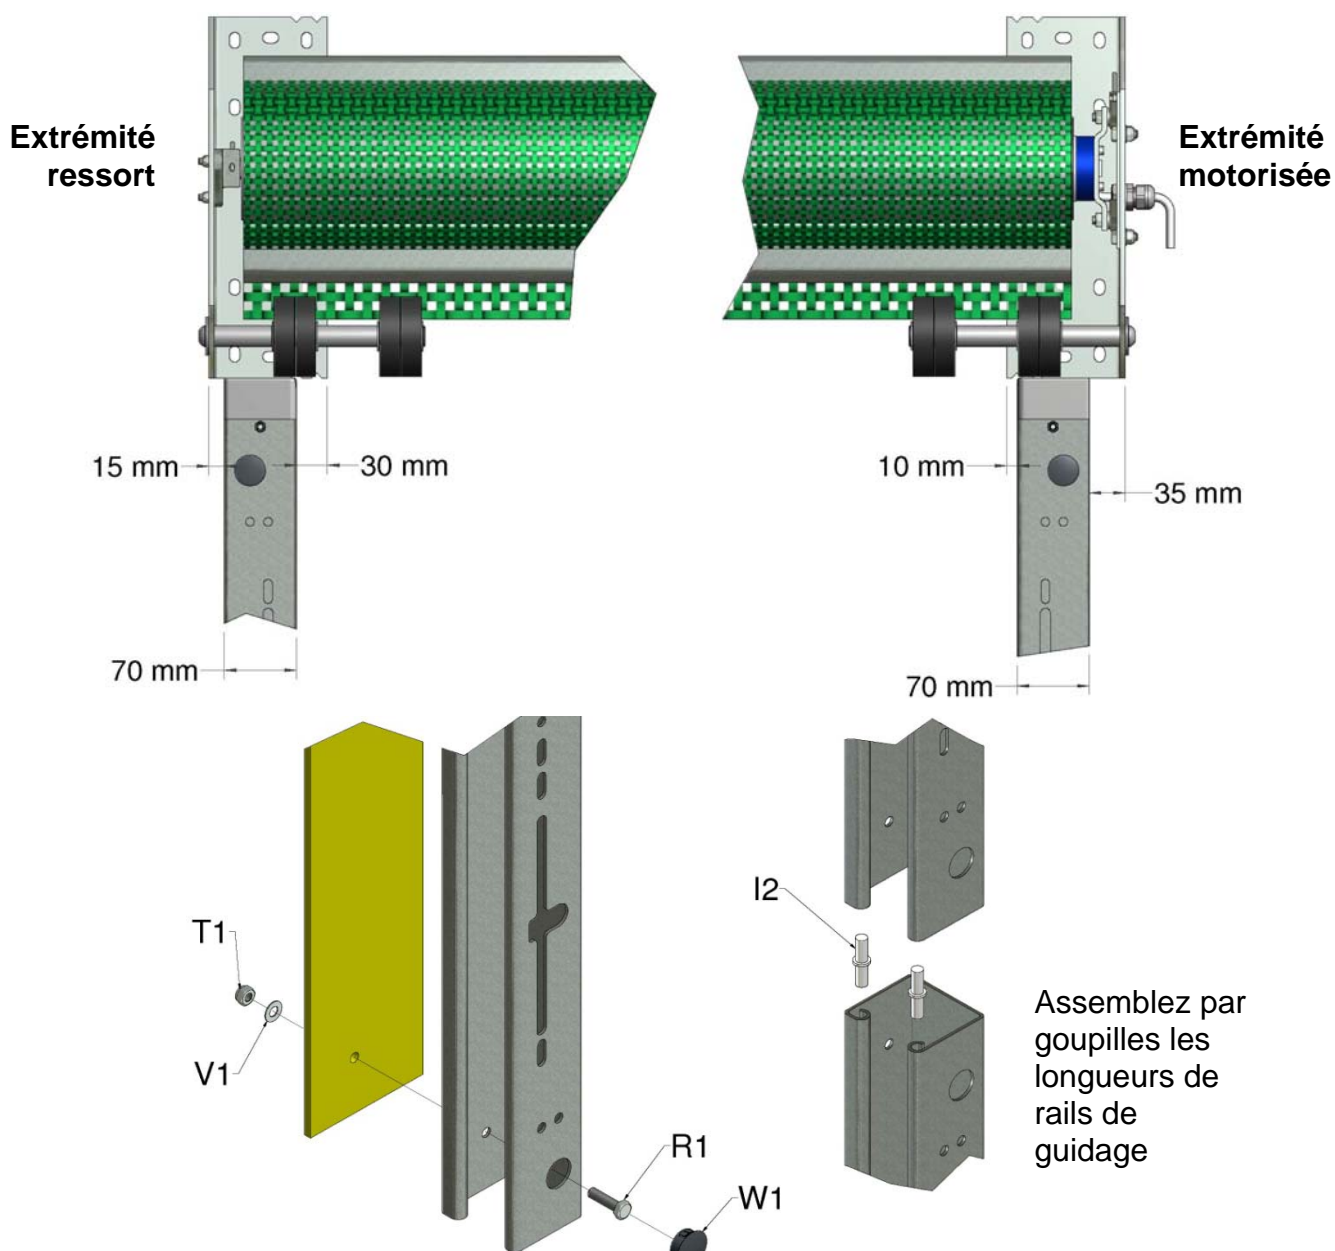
, boulonnage des rails de guidage et assemblage du rail de guidage à la paroi
